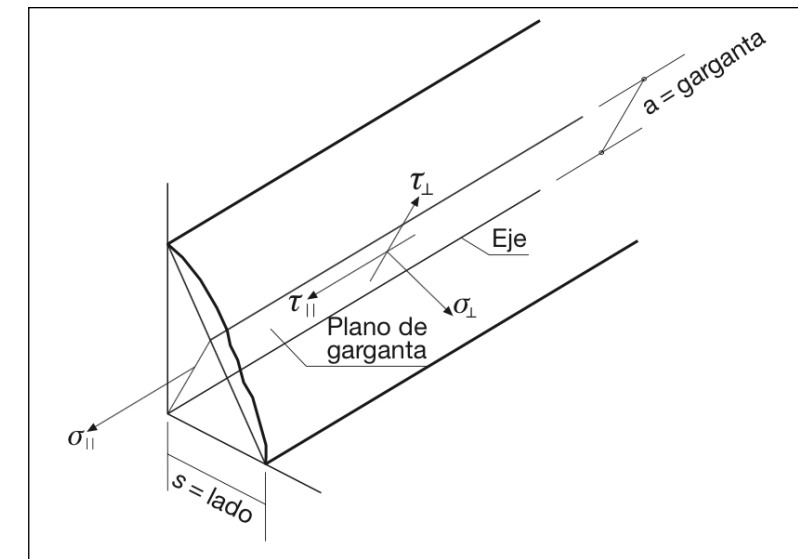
u. Nomenclatura en cordón de soldadura. Fuente: EAE
